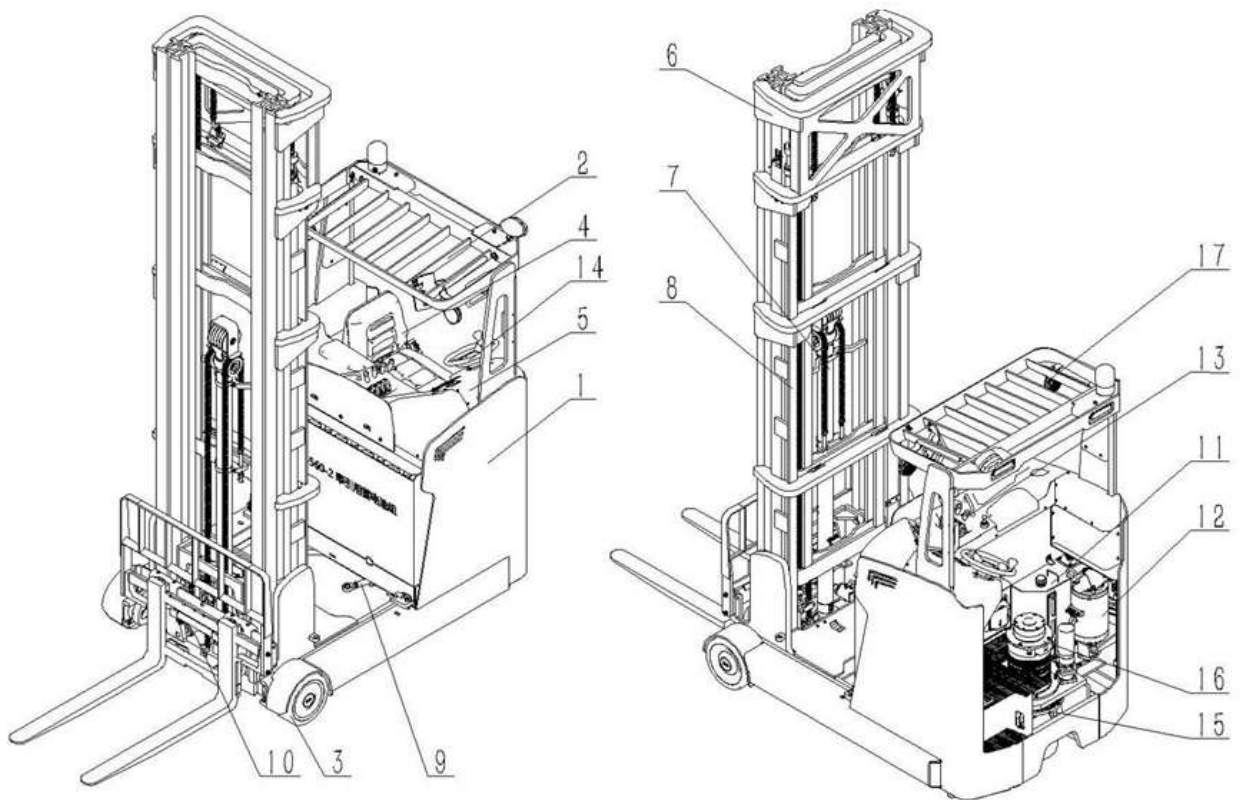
Конструкция рич-трака. Сборочный чертеж:
